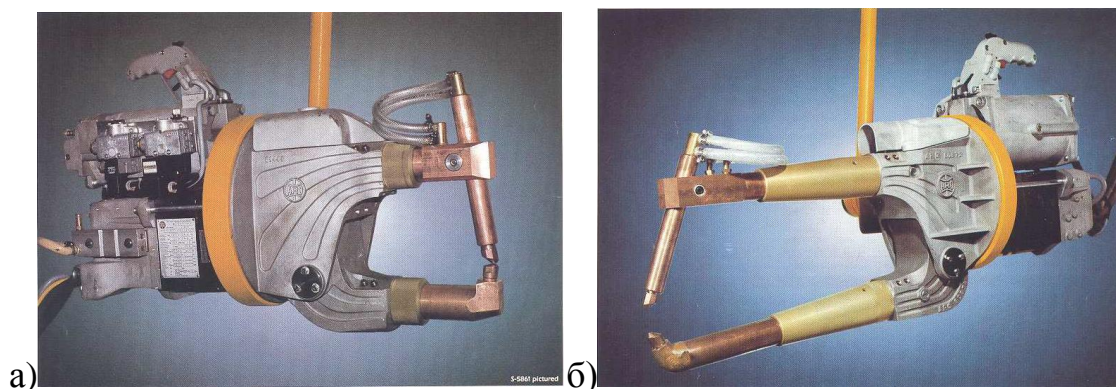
Сварочные клещи TECNA S-5861 (а) и S-6421 (б)
